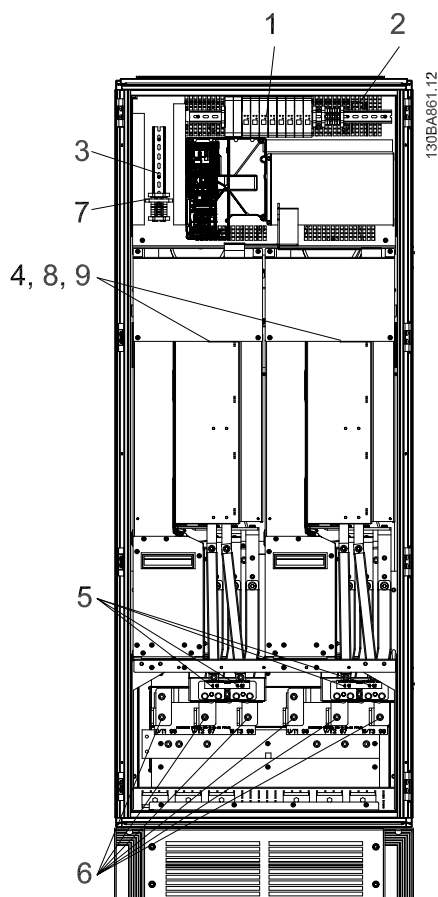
Шкаф инвертора, размер корпуса F1 и F3
